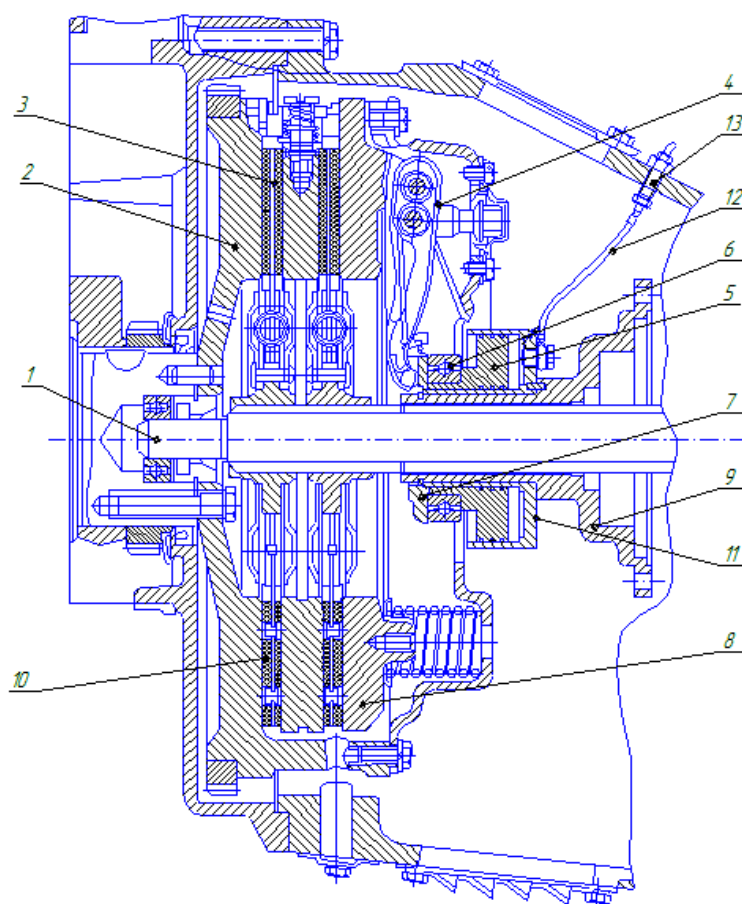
Общий вид модернизированного привода сцепления автомобиля КамАЗ: 1 - вал сцепления; 2 - маховик; 3 - ведомый диск; 4 - отжимной рычаг; 5 - поршень; 6 - выжимной подшипник; 7 - упорное кольцо; 8 - задний нажимной диск; 9 - фланец; 10 - передний ведомый диск; 11 - корпус; 12 - шланг; 13 - переходник.
